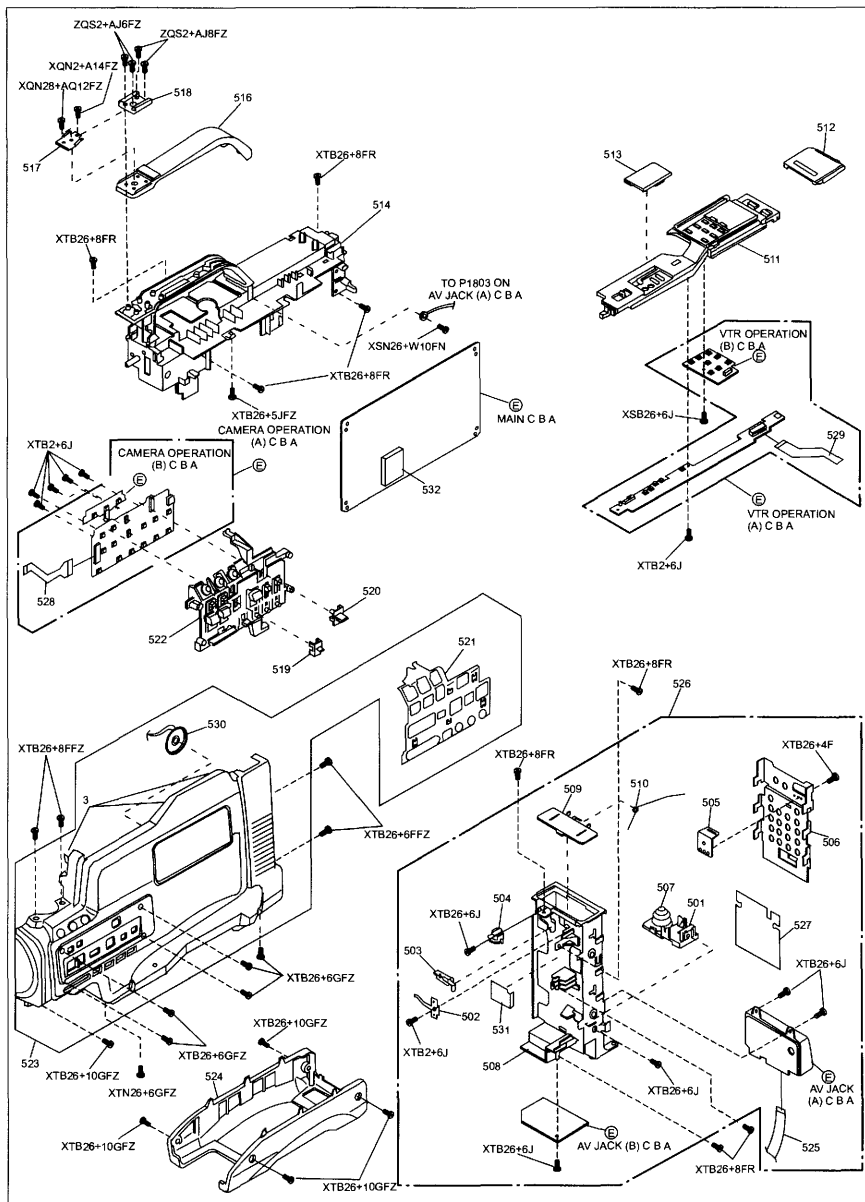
Сборочный чертеж корпуса видеокамер «Panasonic NV-MS4E/В/А, М9000ЕН/МС» (вид слева)
